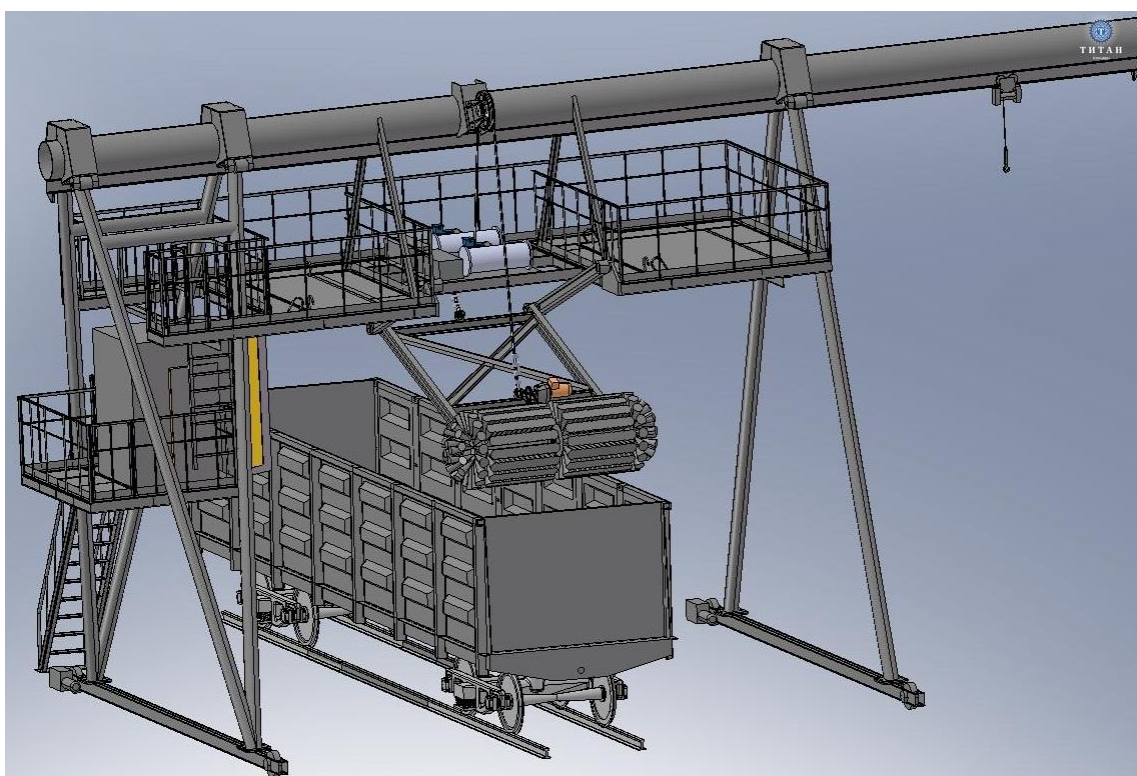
Общий вид щёточной машины МЩ-10 очистки полувагонов
